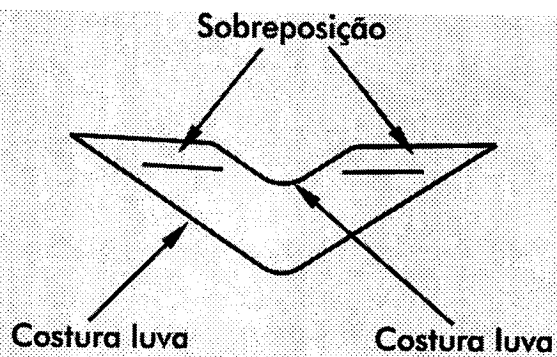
Desenho técnico da peça 2 do meio do 2º e 3º dedo
